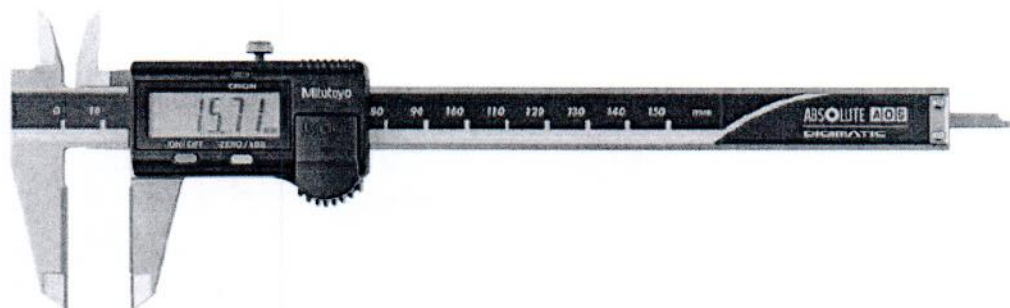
Внешний вид штангенциркуля AOS ABSOLUTE Digimatic серии 500 с твердосплавными губками
